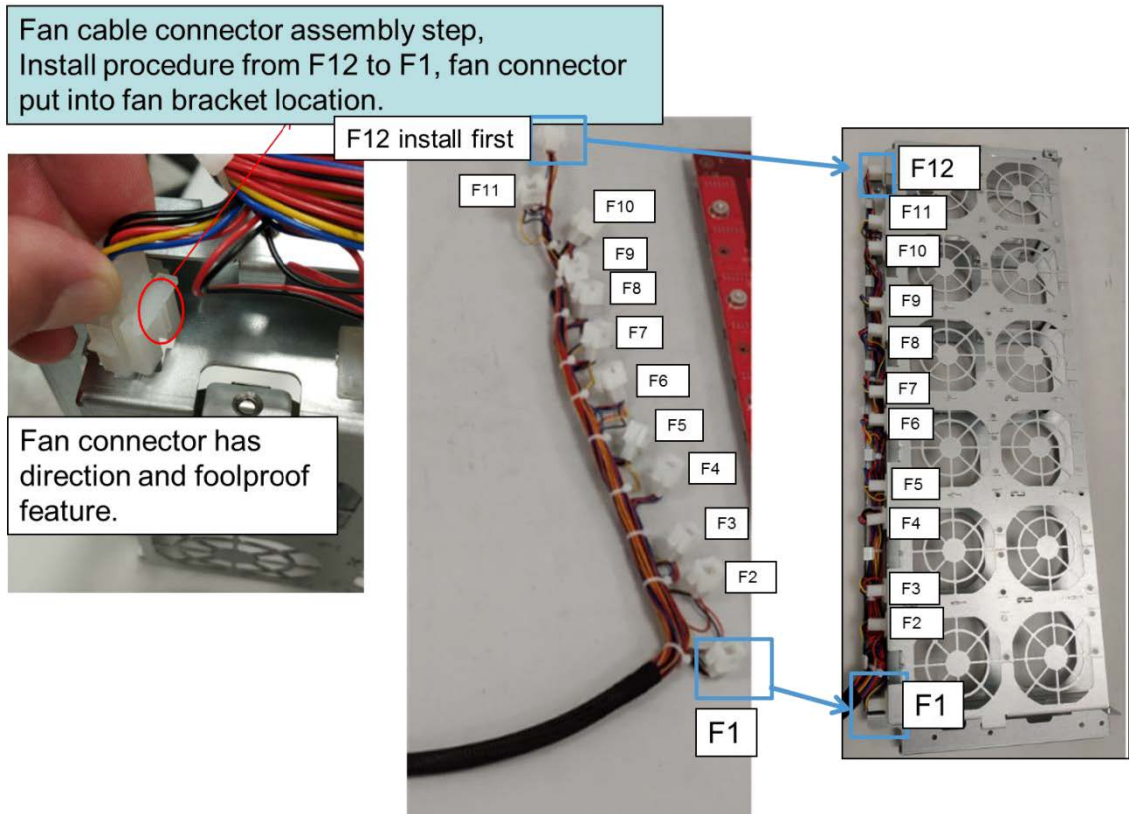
Assemblage du câble de ventilateur vers le support de ventilateur
